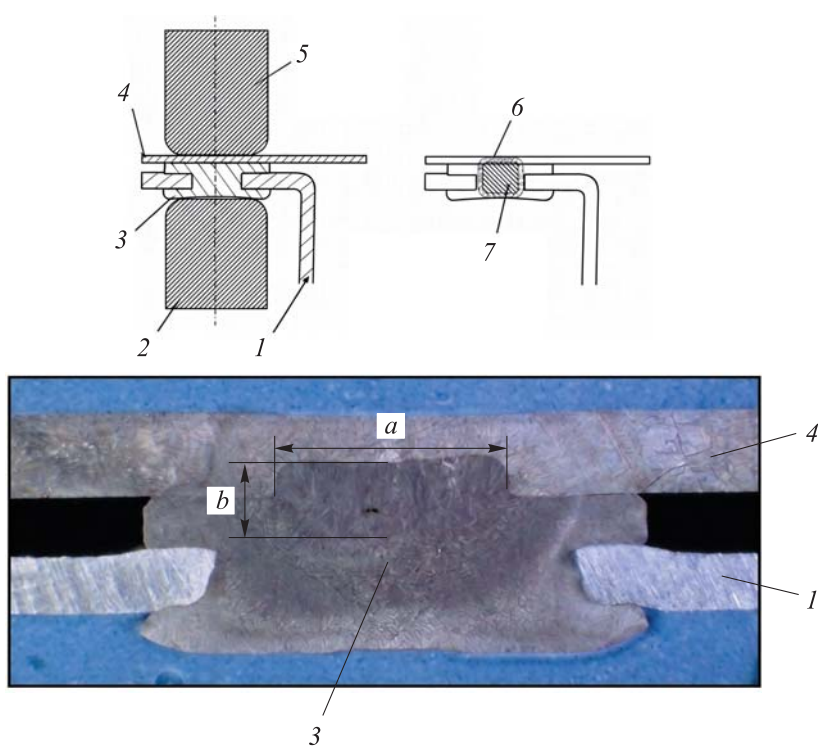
Схема конструкции точек заклепочной сварки:
